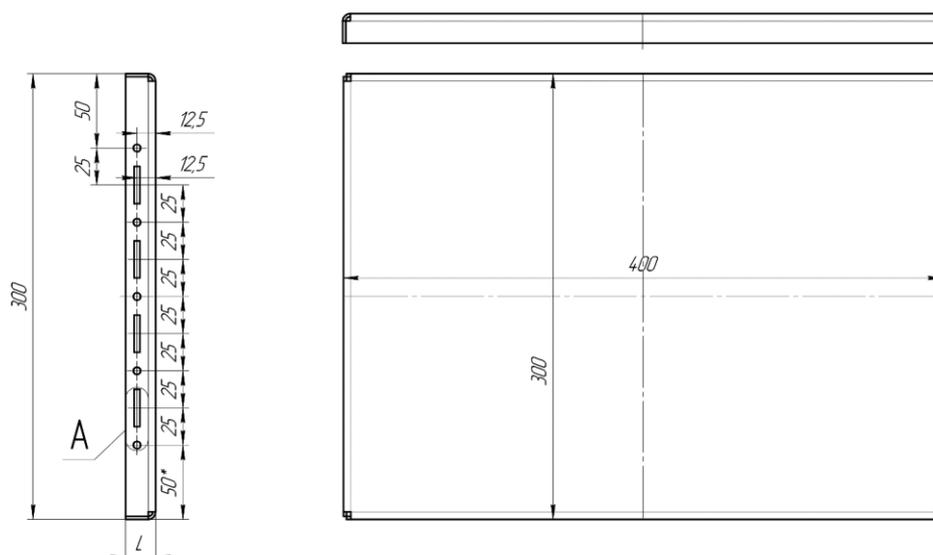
Пример конструкции знака с универсальными отверстиями для крепления.
